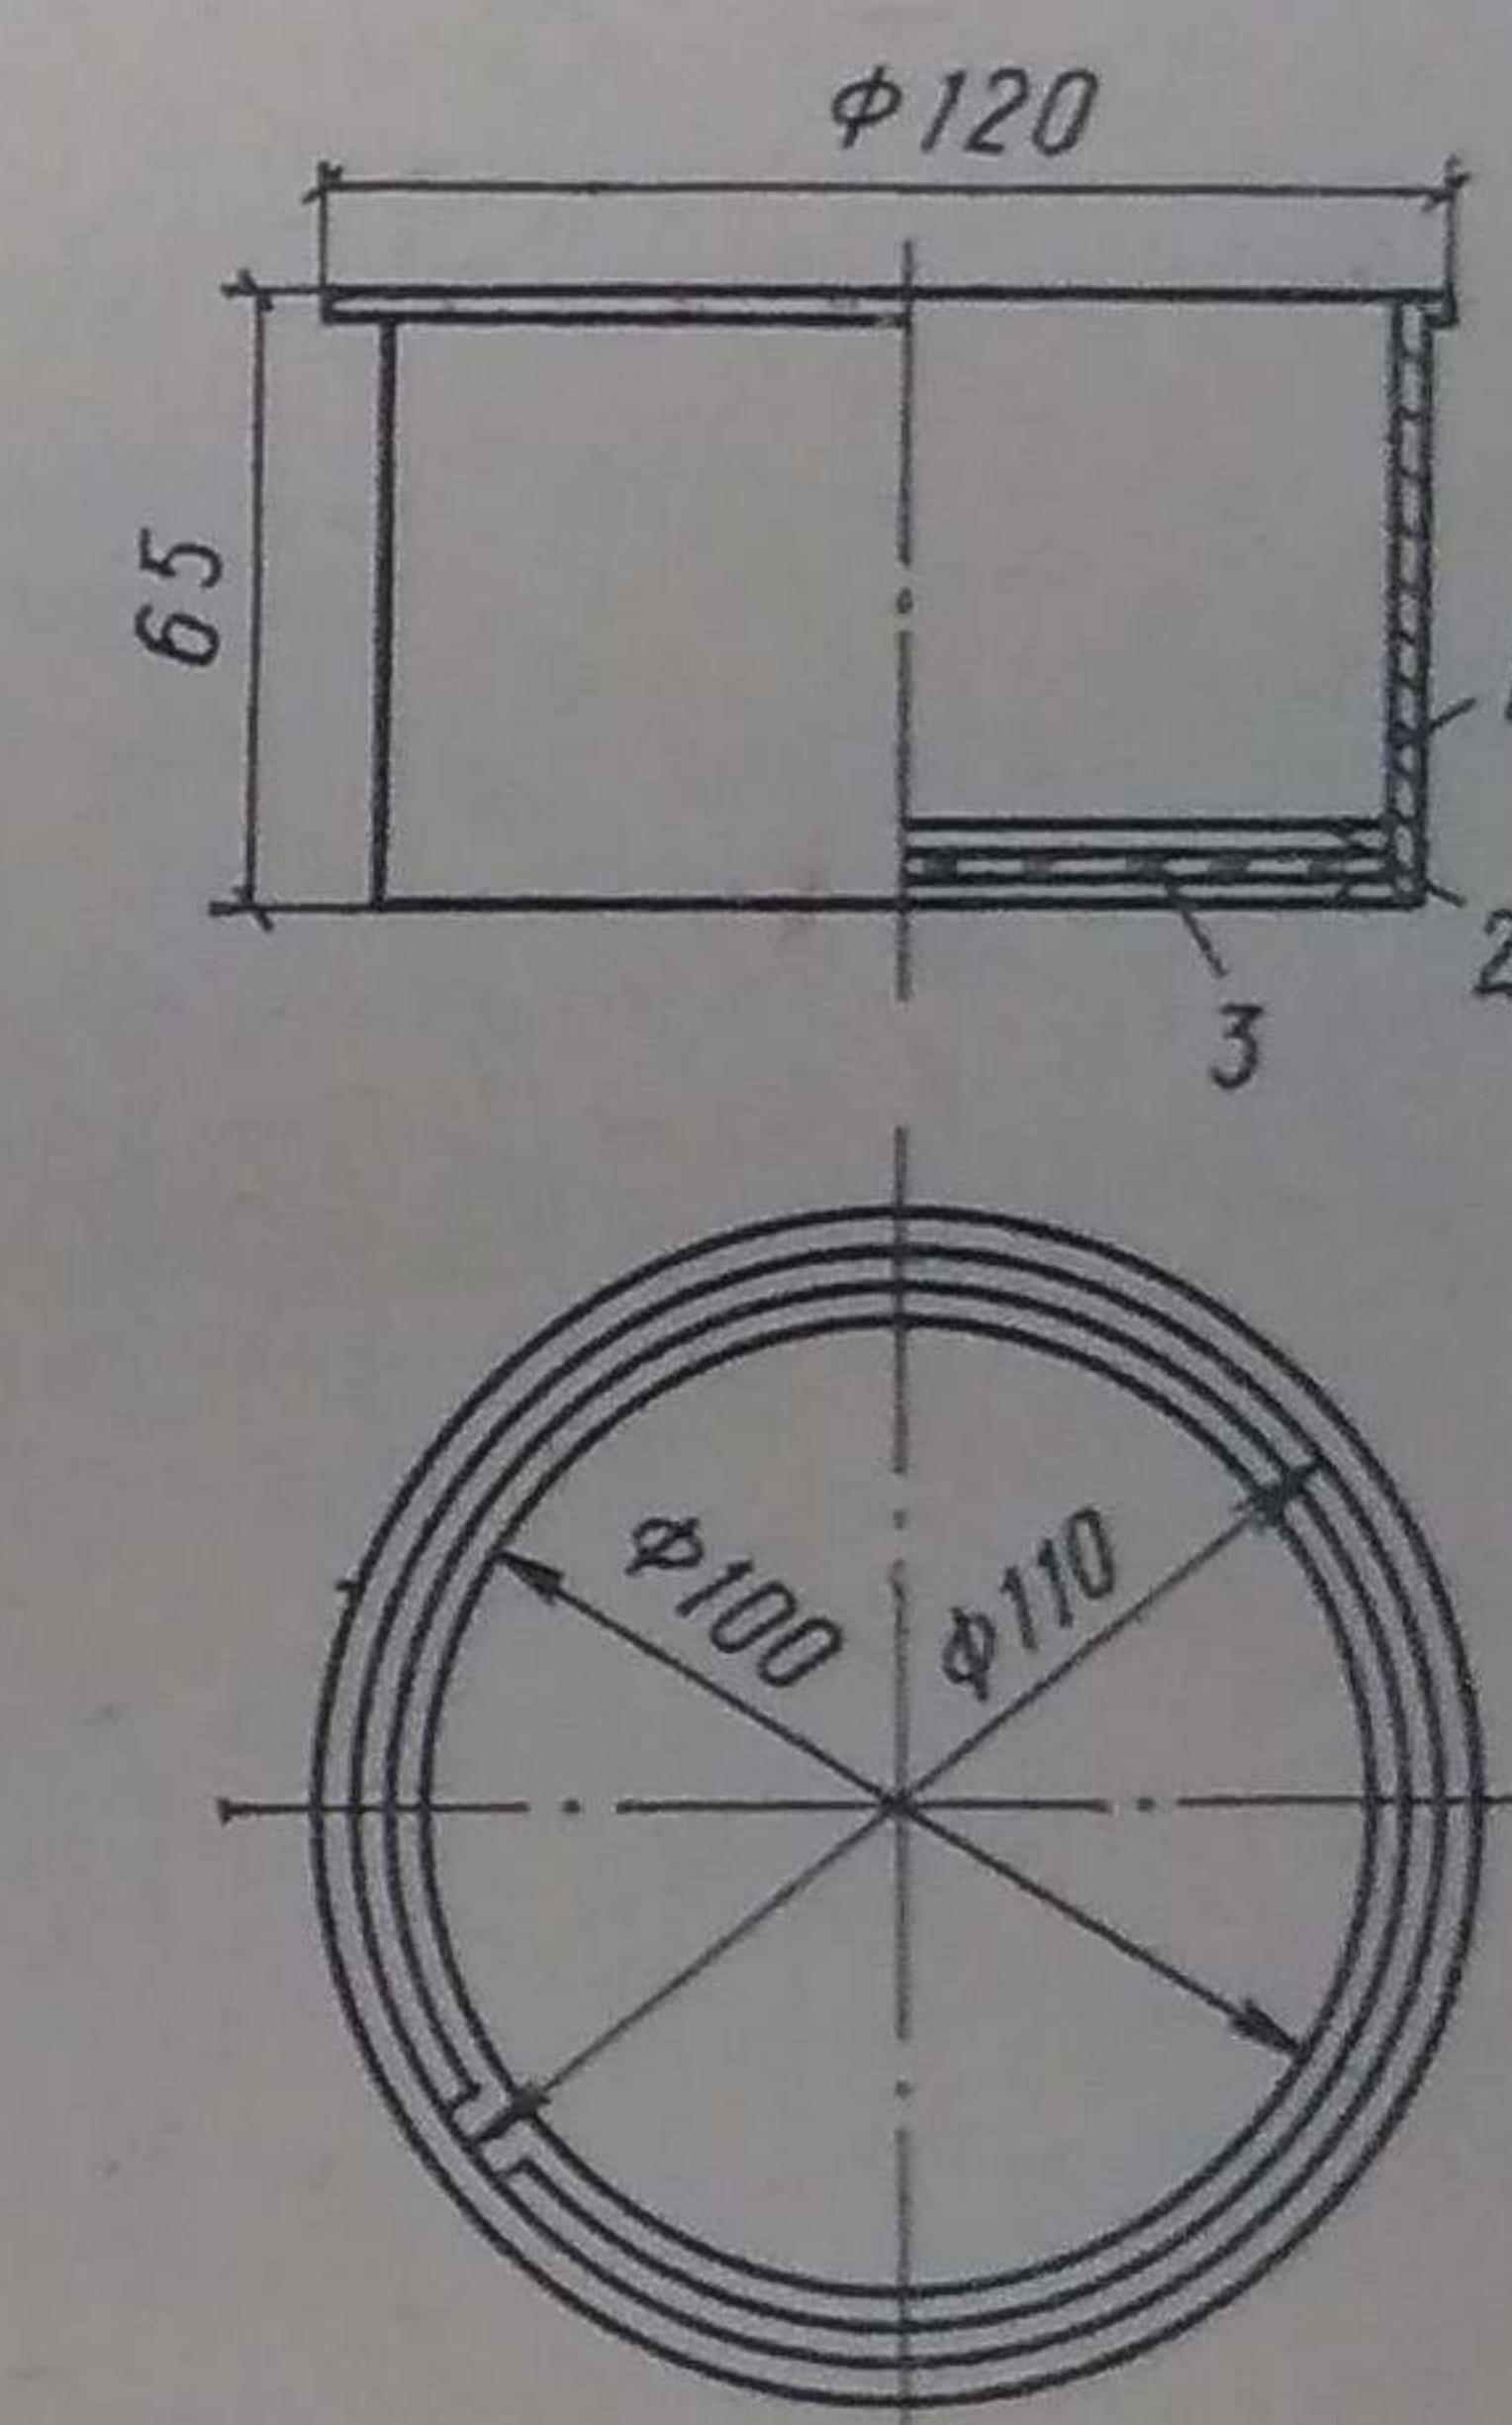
Маскировочное приспособление для светильников наружного освещения
